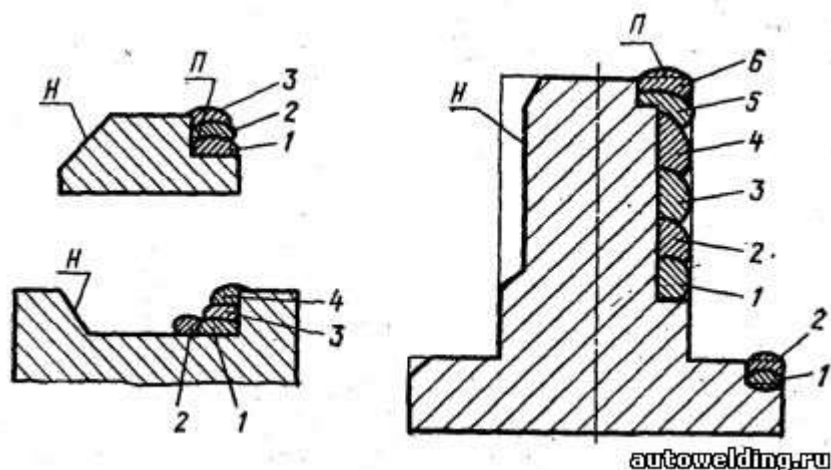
Правильная (П) и неправильная (Н) подготовка поверхностей под наплавку;
